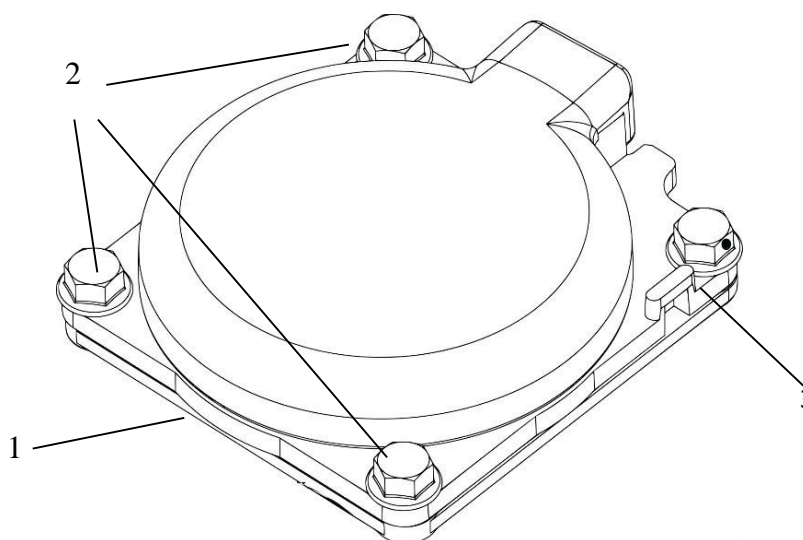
Монтаж ДУТ – крепление шурупами
